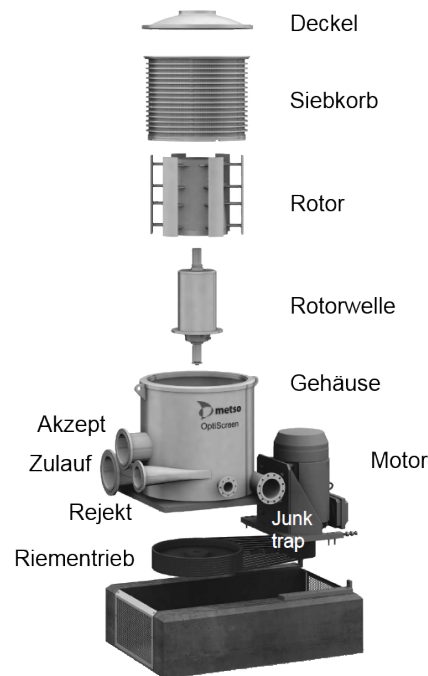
Explosionszeichnung eines Drucksortierers adaptiert [30]
